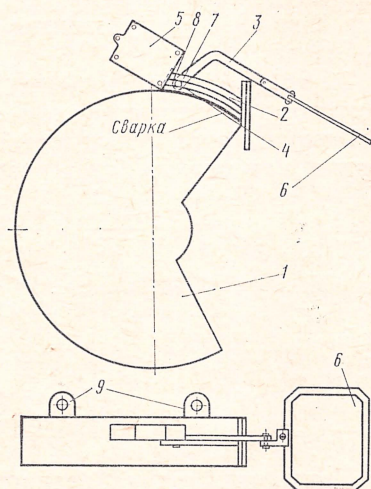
Блокировочное приспособление к шлифовальному кругу
